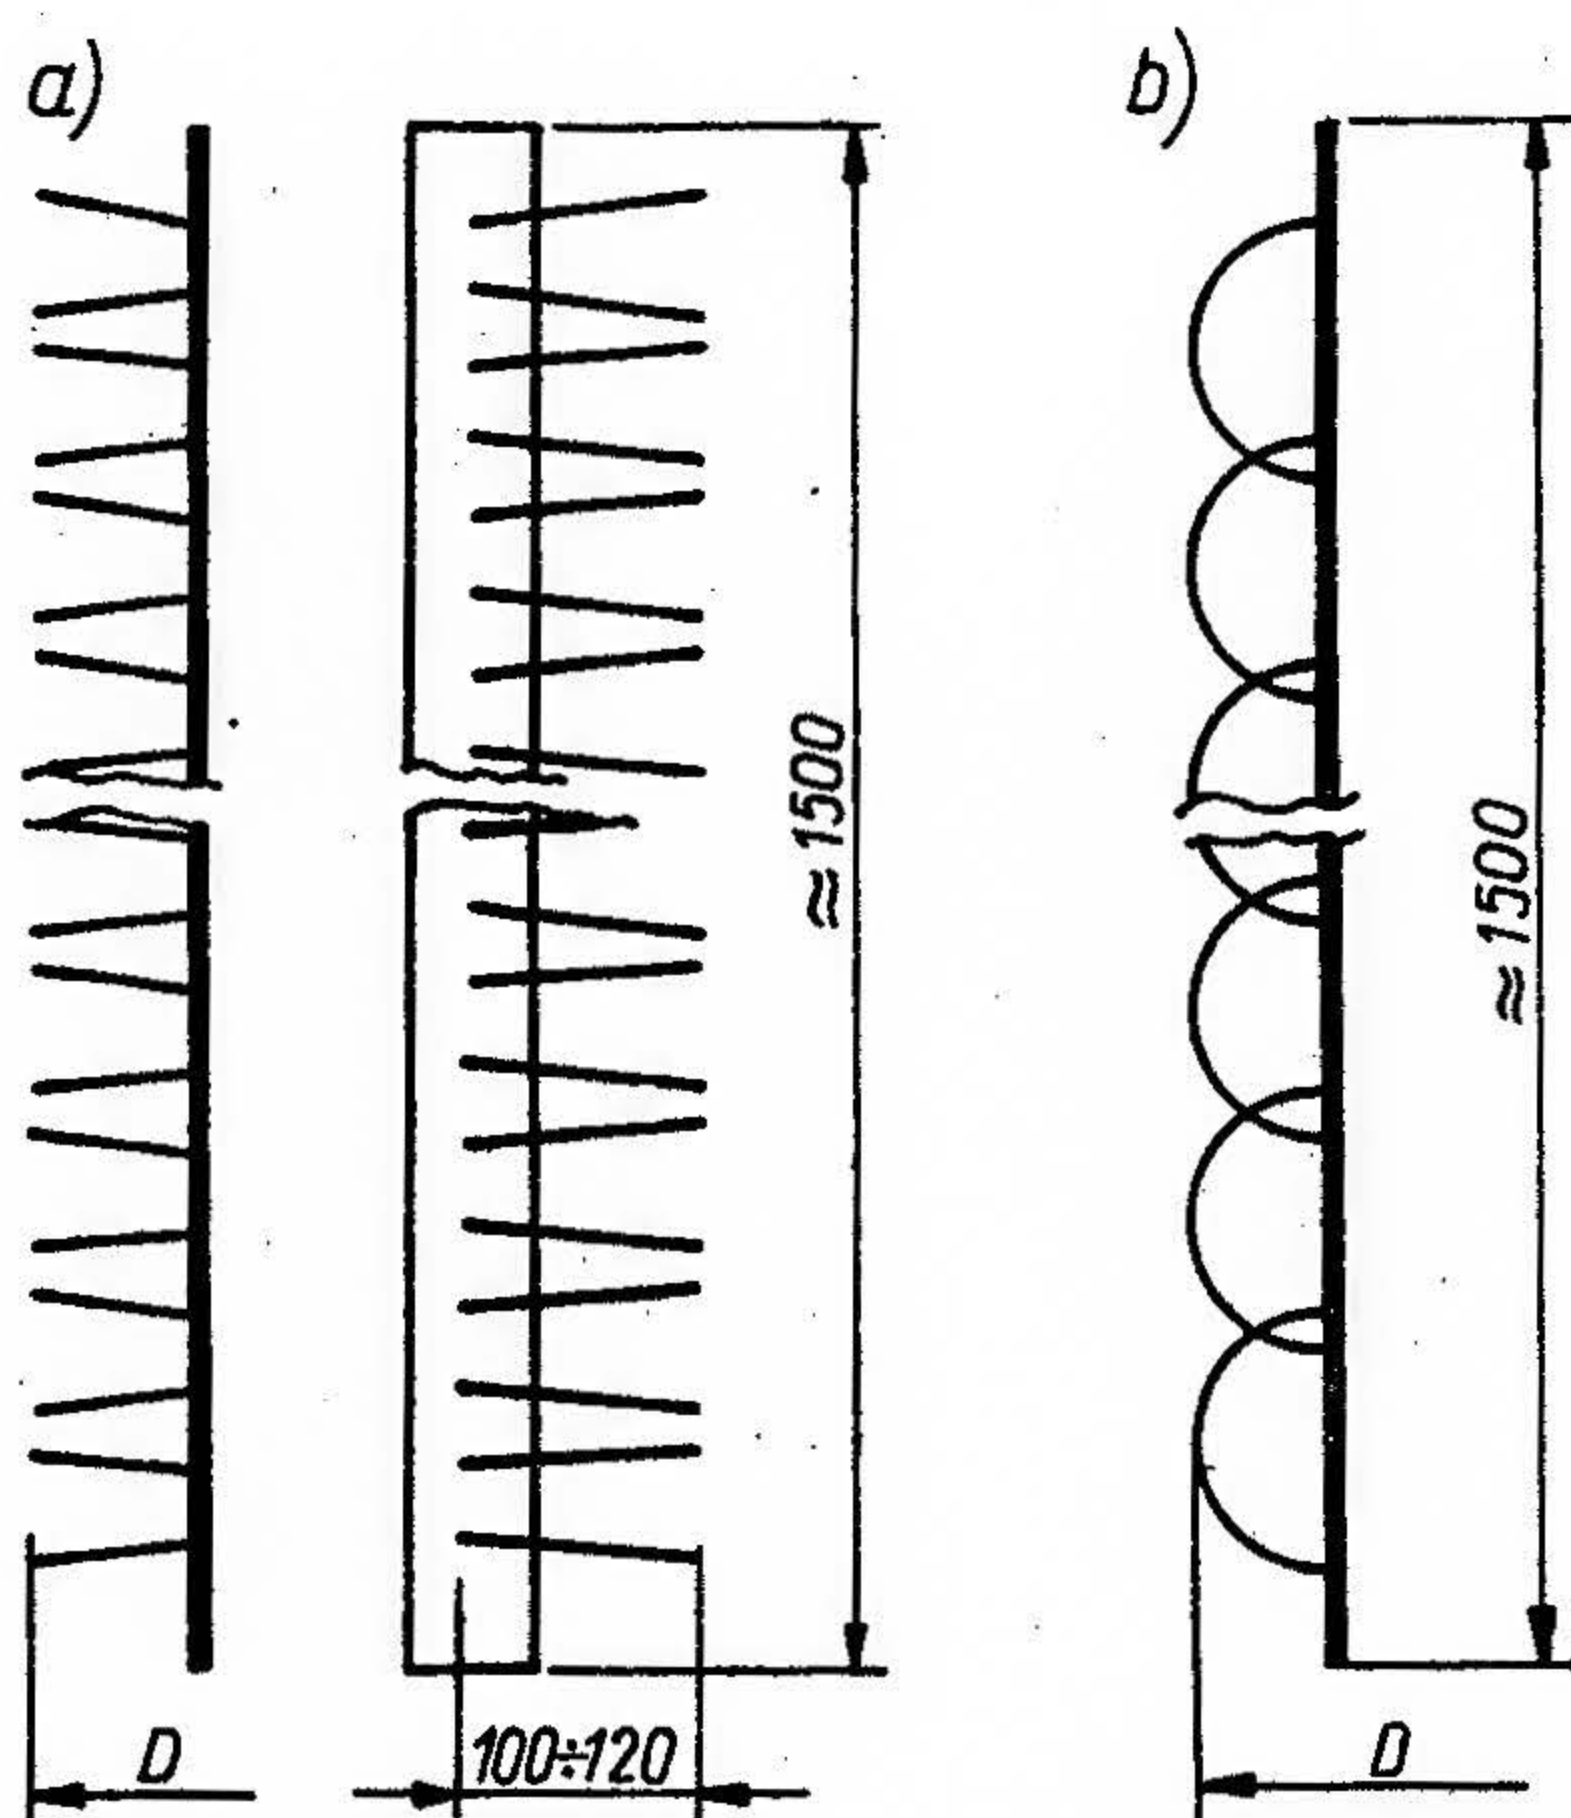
Przykładowa konstrukcja skrobaka pierścieniowego z pętlami
